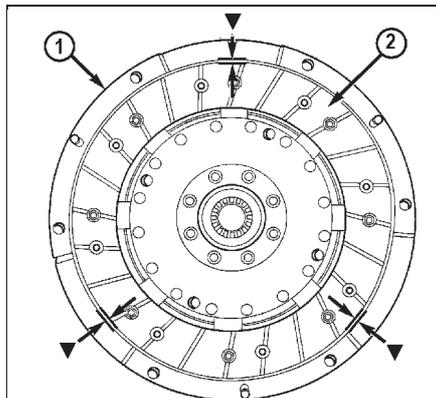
в. Установка диска сцепления. Модель 2.4L с наддувом. 1 - маховик, 2 - диск сцепления, ► - обеспечить равное расстояние.
